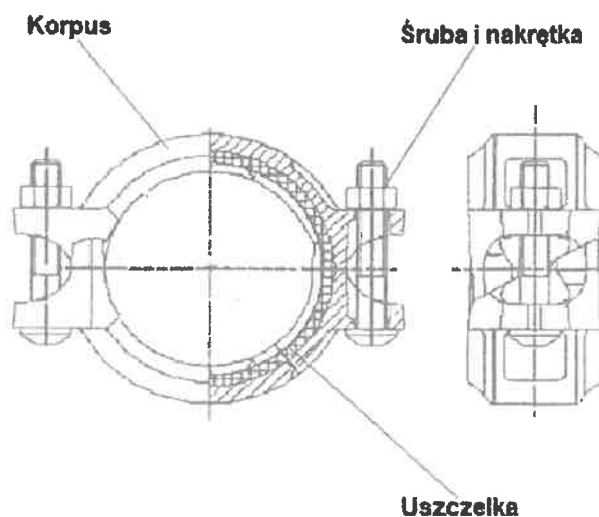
Konstrukcja – złącza typu GKS i GKF
